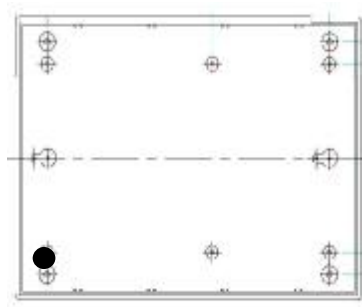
Корпус отсчетного устройства, вид снизу
